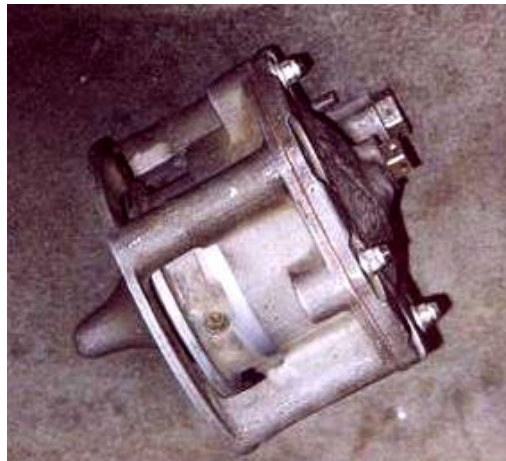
Partes internas de la sección de engranaje de reducción
